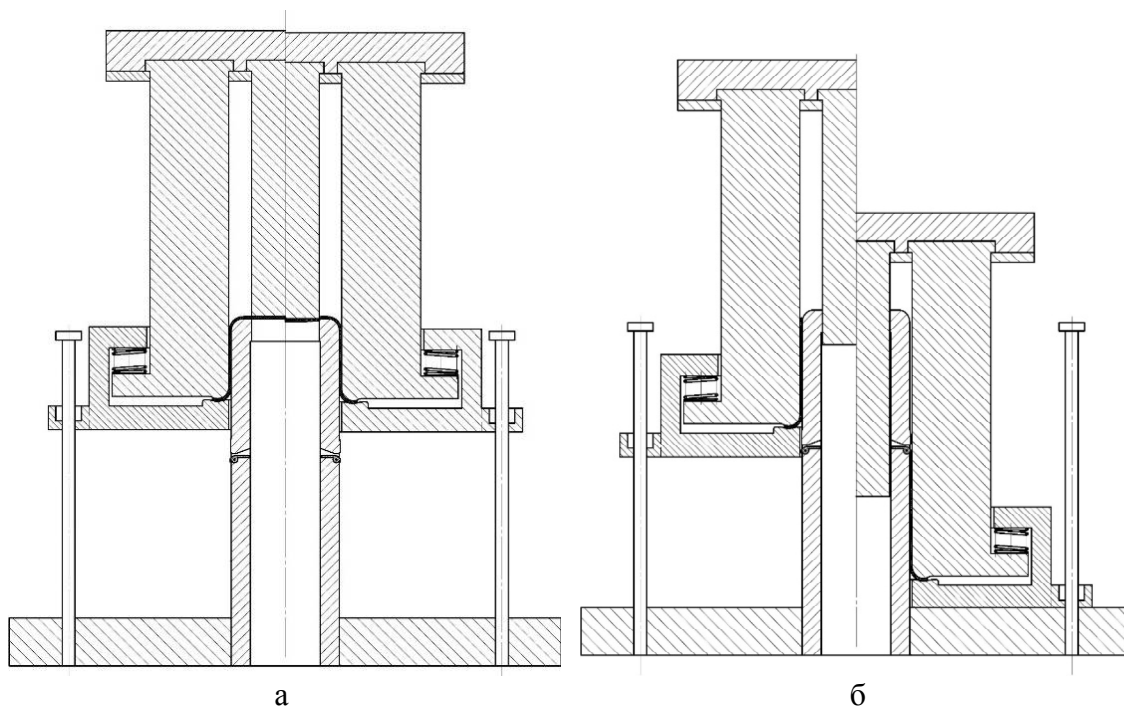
Стадии штамповки: а — вытяжки и пробивки, б — отгибки и протяжки
